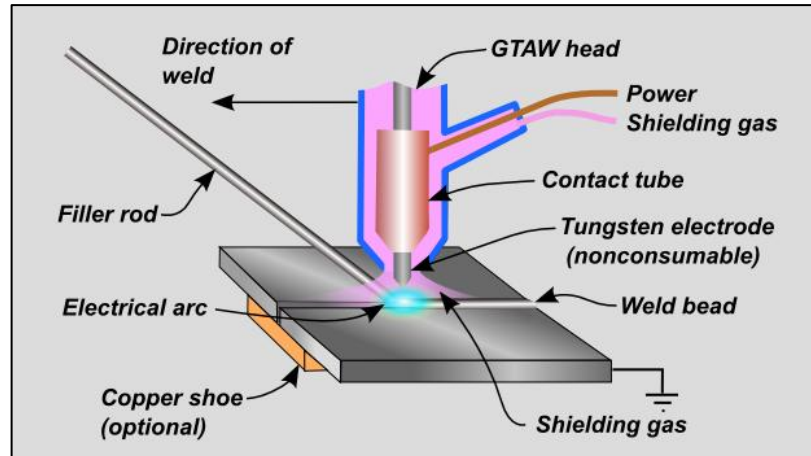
2: Diagrama esquemático del proceso de soldadura GTAW
